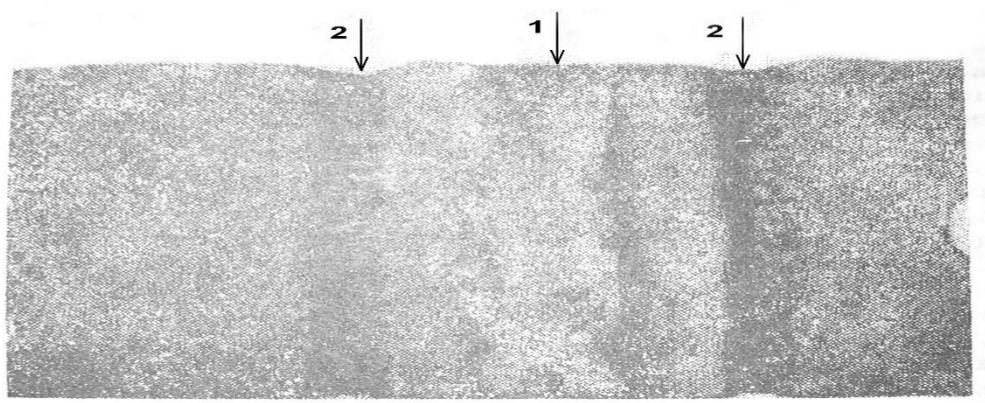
Коррозионное разрушение стальной конструкции в области сварного шва:
